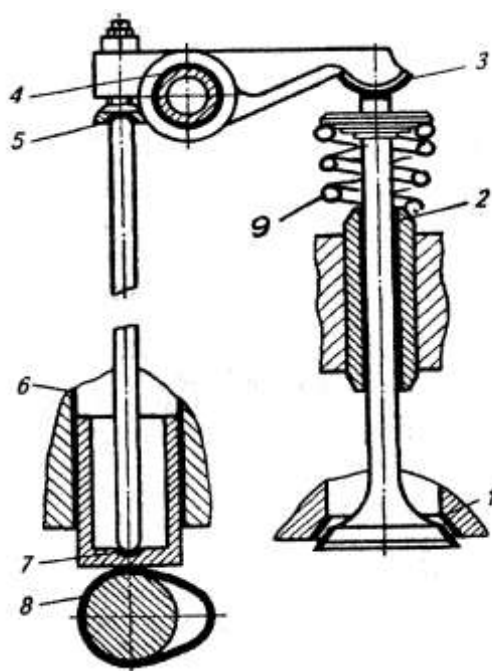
Схема изнашивающихся соединений механизма газораспределения:
